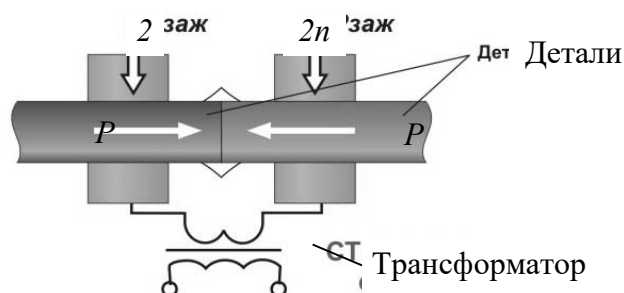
Схема стыковой сварки давлением
